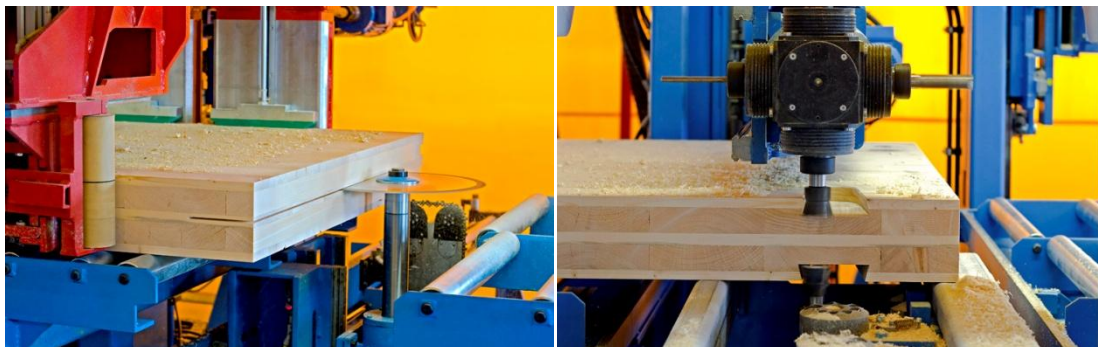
Maquinas de replanteo y manufacturas sobre productos de madera mediante sierras.
